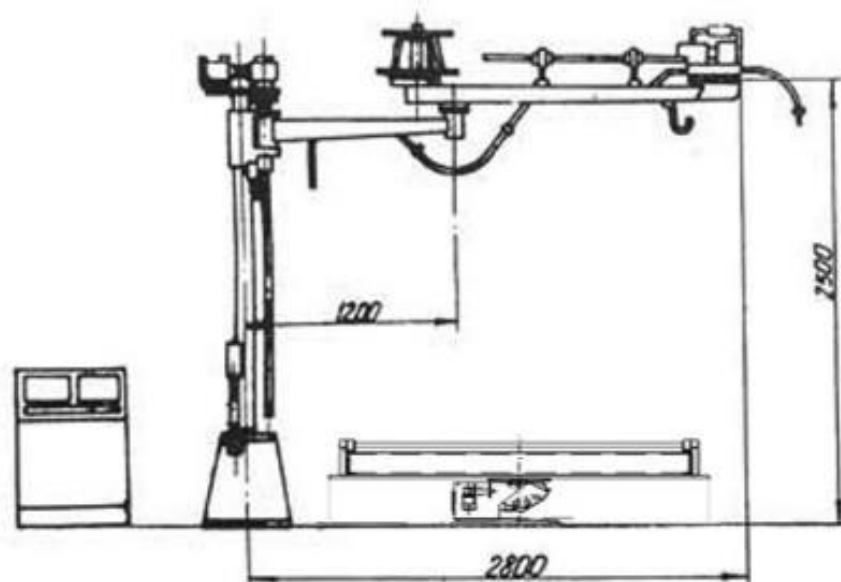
Установка для зварювання каркасу рами борта
